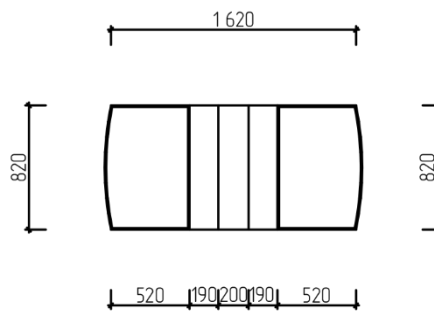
Чертеж оборудования. Вид сверху
